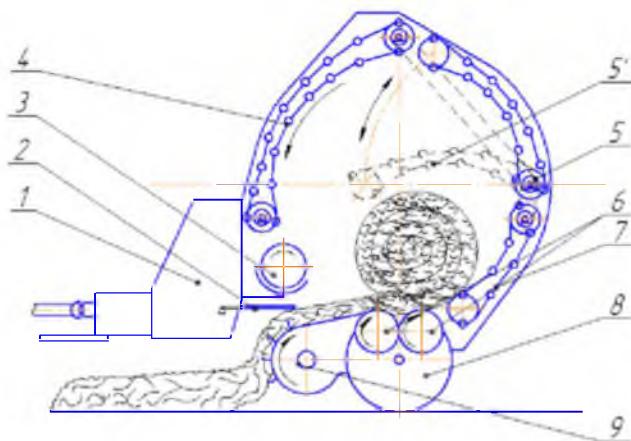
Рулонный пресс-подборщик с модернизированной пресс-камерой:
